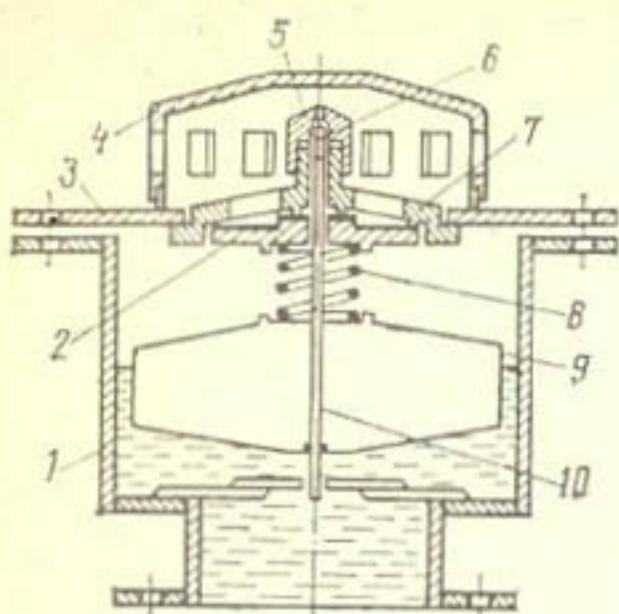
Универсальный вантуз конструкции ЛИИЖТ:
